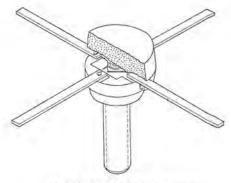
MTM 360 の断面 Cutaway drawing of MTM 360
